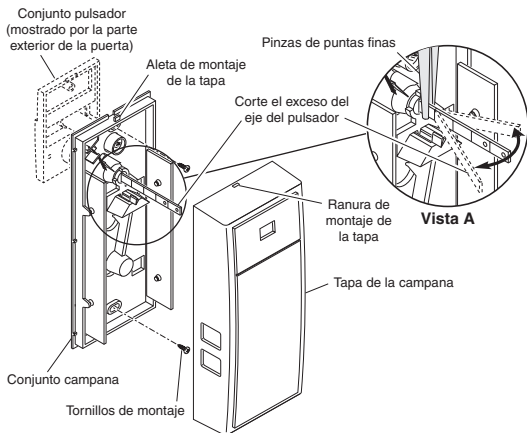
Montaje del conjunto campana y acople de la tapa de la campana
